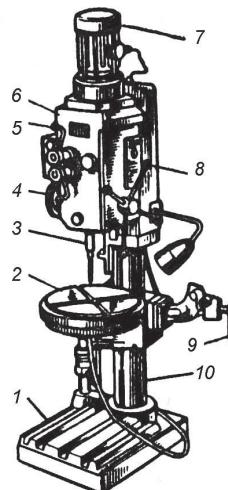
Універсальний вертикально-свердлильний верстат:
